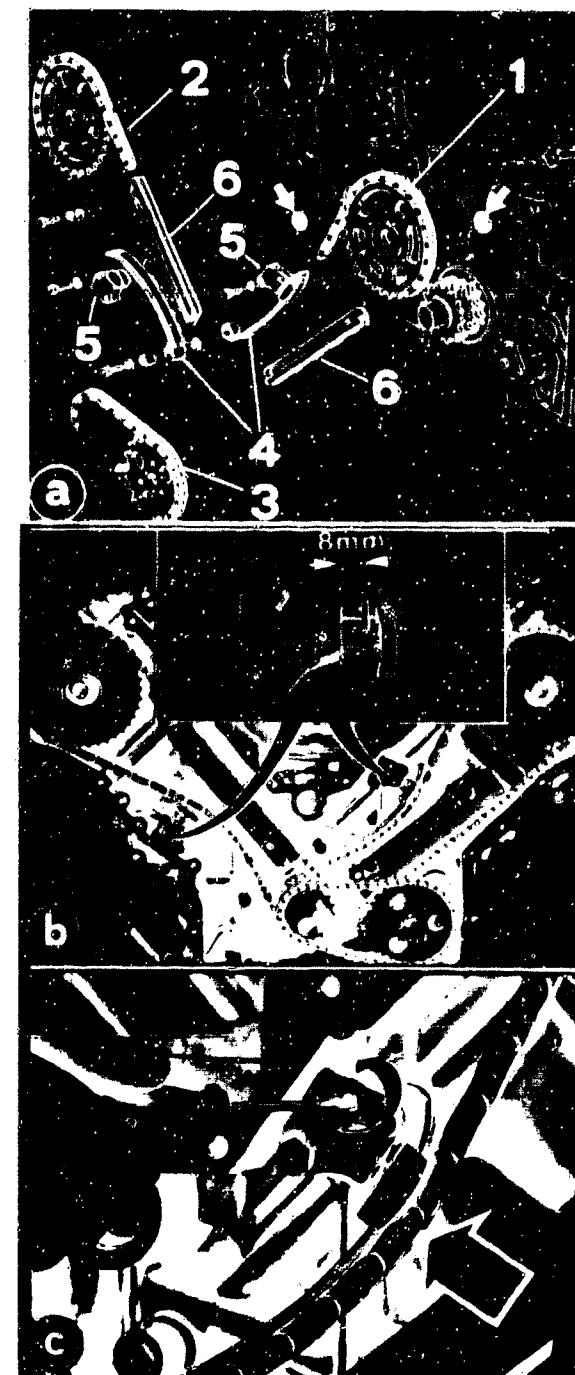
B 28 V 6-Motor: a) Teile der Motorsteuerung: 1/2 linke/rechte Steuerkette – 3 Ölpumpenantrieb – 4 Spannschienen – 5 Hydraulischer Kettenspanner (Olsieb beachten!) – 6 Führungsschienen – b) Wenn der Gleitschuh des Kettenspanners mehr als 4 Zähne (8mm) aus dem Gehäuse ragt, sind die Ketten zu stark gedehnt und müssen ersetzt werden. – c) Durch Eindrücken des Kolbens und Drehen des Sperriegels um 90° wird dieser ausgeklinkt.
